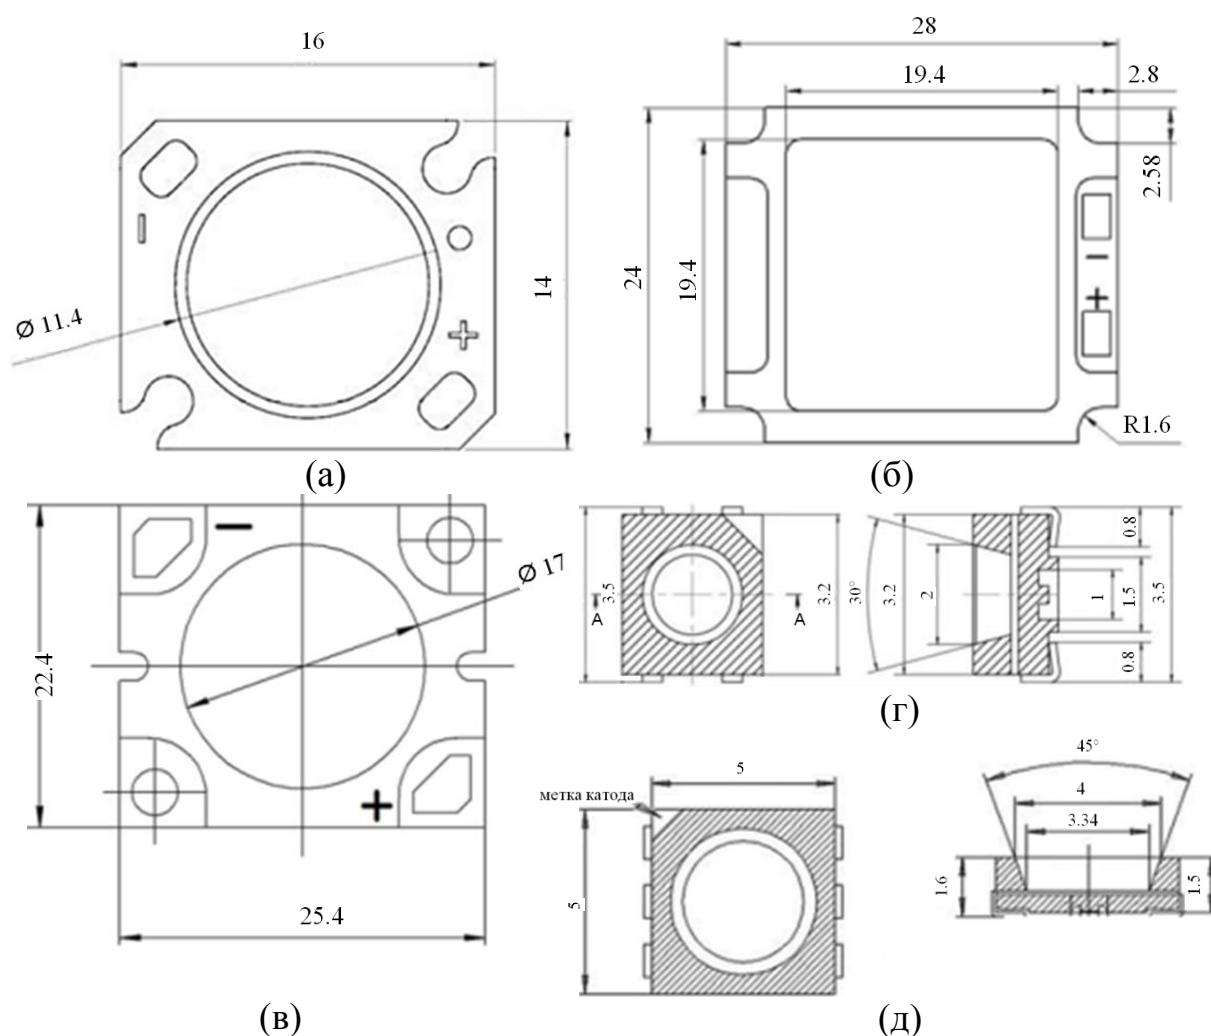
Виды корпусов светодиодов: корпус на металлическом или керамическом основании для устройства «чип на плате» (а–в), вид сверху; корпус из PMMA для светодиода высокой яркости (г, д), вид сверху и сбоку. Размеры на чертежах указаны в мм.
